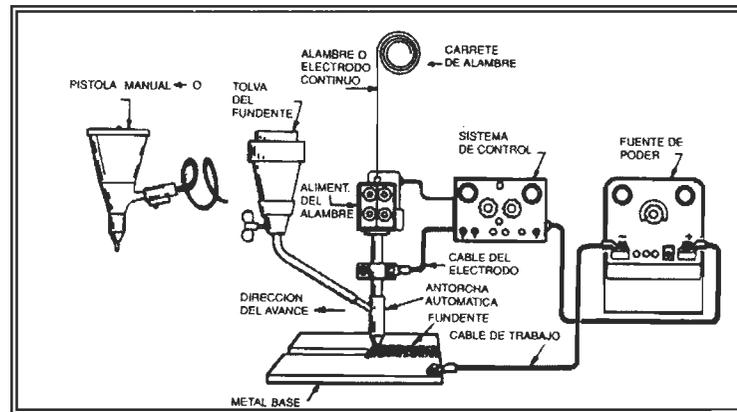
Equipo para soldadura de arco sumergido
